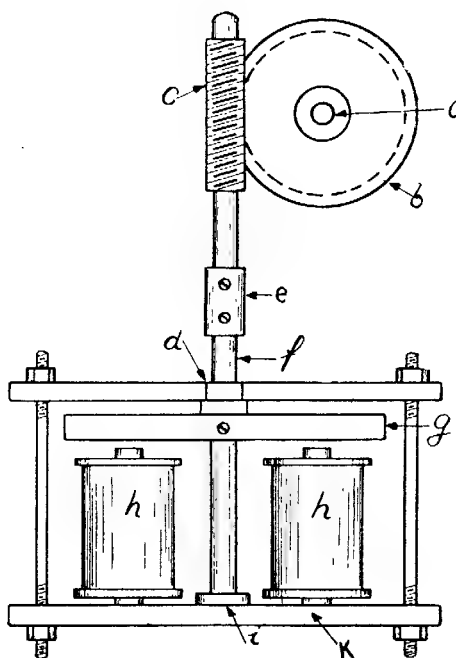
Сцепление синхронного моторчика с понижающим оборот-устройством (ниточной моталкой треста Госшвеймашина). а — ось привода барабана, б — шестеренка, скрепленная наглухо с муфтой, сидящей на валу рабочего барабана, в — ведущий червяк, д — медный вкладыш, е — муфта со стопорными винтами на обеих осях (мотора и червяка передачи), ж — ось моторчика, з — ротор, насаженный на ось стопорным винтом, и — электромагниты статора, л — пятая, к — железное основание
